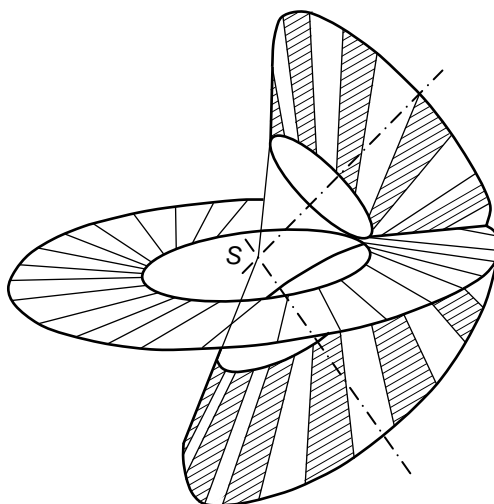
Engrenagem cônica de dentado helicoidal.
